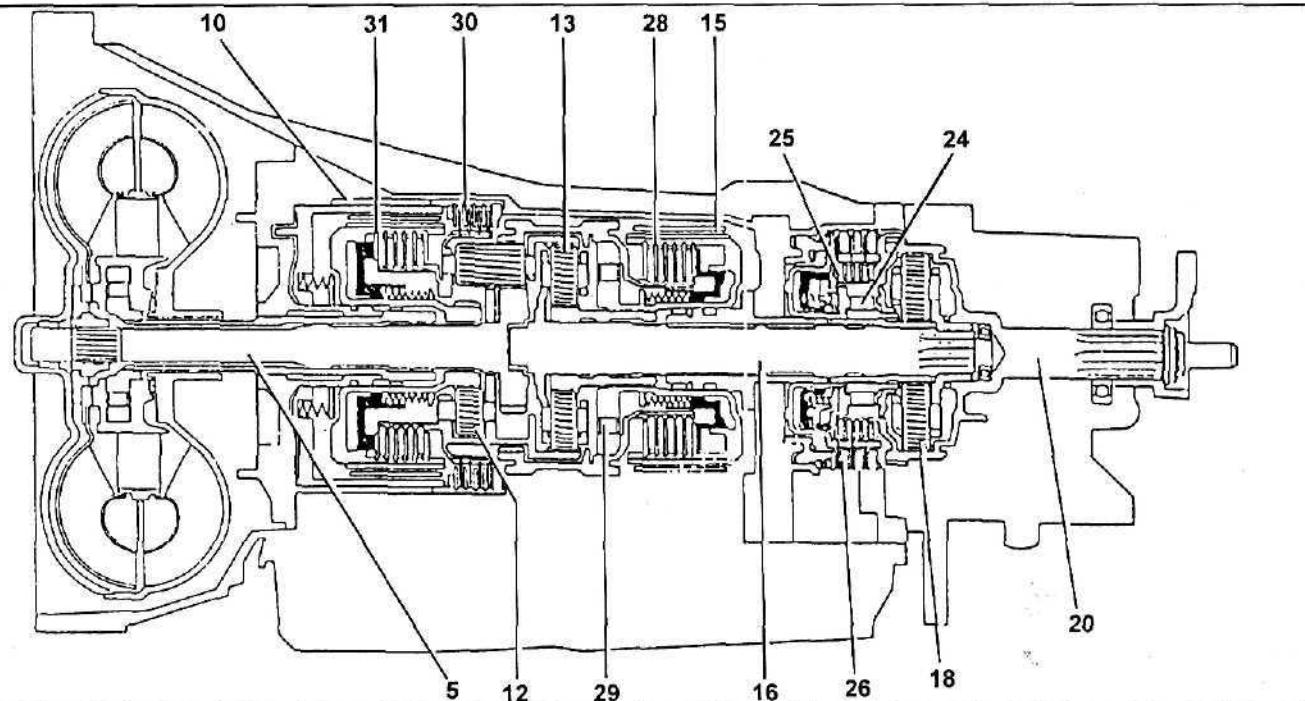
Автоматическая коробка передач 722.5. 5 - Ведущий вал, 10 - Ленточный тормоз B1, 12 - Планетарный ряд со сцепленными сателлитами, 13 - Средний планетарный ряд, 15 - Ленточный тормоз B2, 16 - Промежуточный вал, 18 - Повышающий планетарный ряд, 20 - Ведомый вал, 24 - Муфта свободного хода F2, 25 - Блокировочная муфта KS, 26 - Дисковый тормоз BS, 28 - Блокировочная муфта K2, 29 - Муфта свободного хода F1, 30 - Дисковый тормоз B3, 31 - Блокировочная муфта K1.
